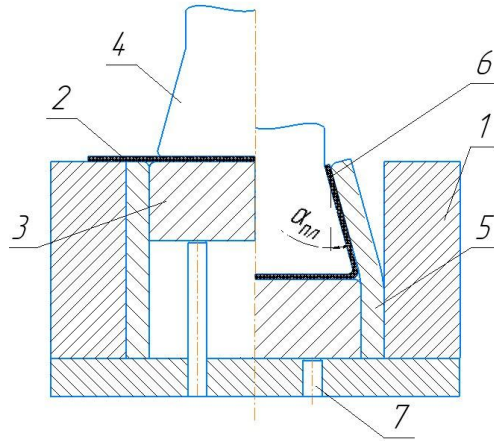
Схема двухугловой гибки с использованием упругих билинейных планок (слева начало процесса, справа окончание): 1 – матрица, 2 – заготовка, 3 – выталкиватель, 4 – пуансон, 5 – упругие планки, 6 – деталь, 7 – шпильки
